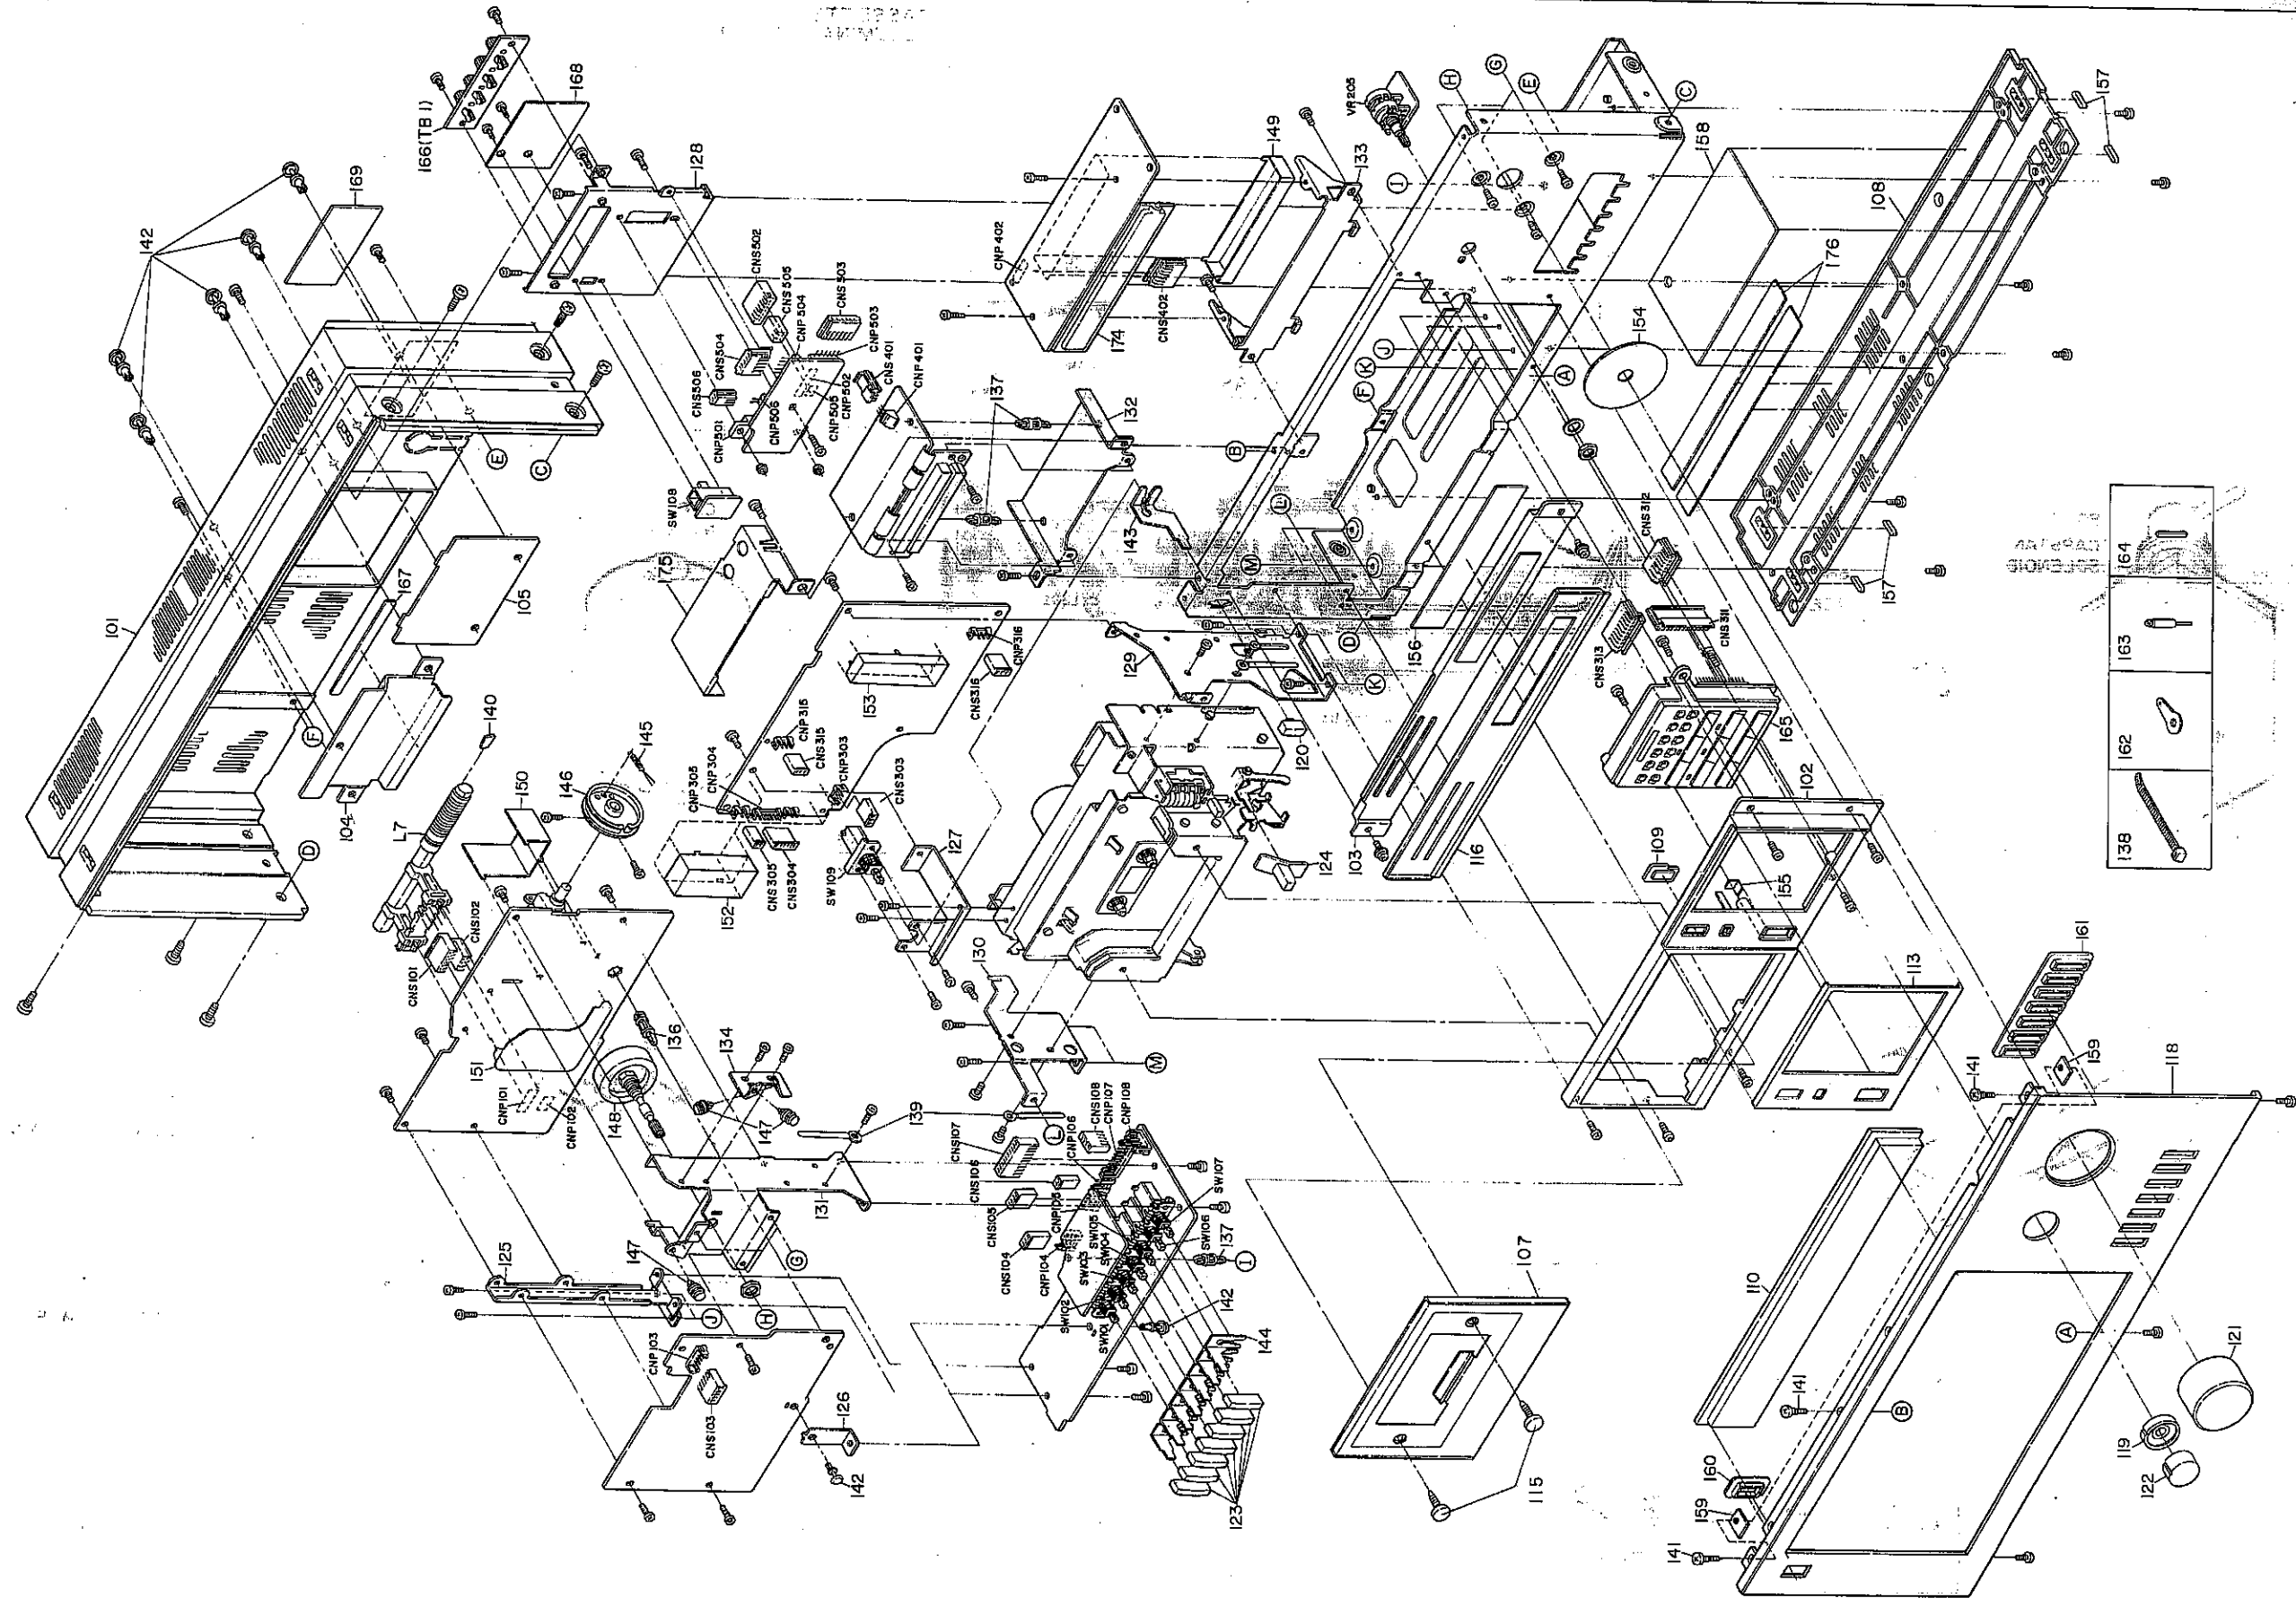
EXPLOSIONSDARSTELLUNG DES GEHÄUSES
